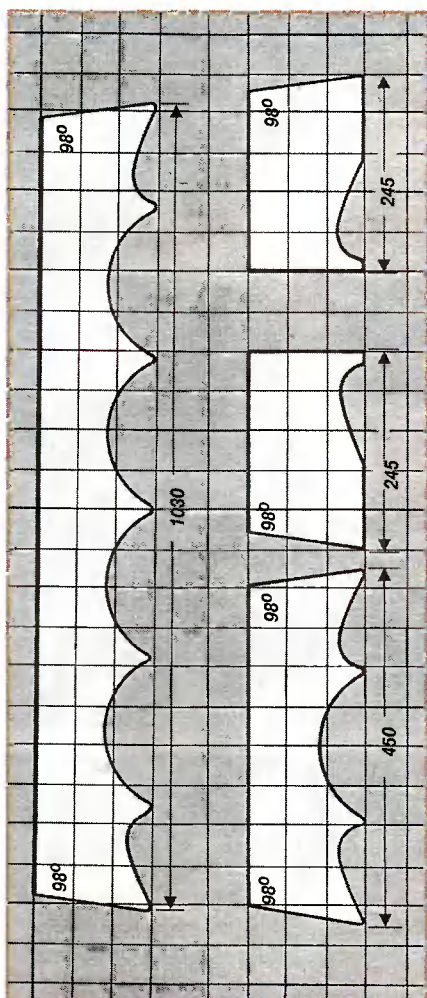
Шаблоны деталей стола. Пунктирной линией обозначен размер заготовки (доски), из которой выпиливают ножку.
